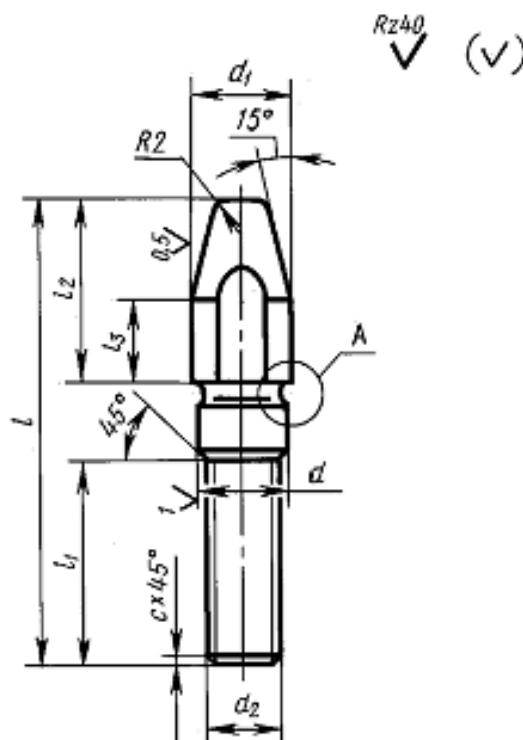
Направляющий штырь с резьбовым хвостовиком
